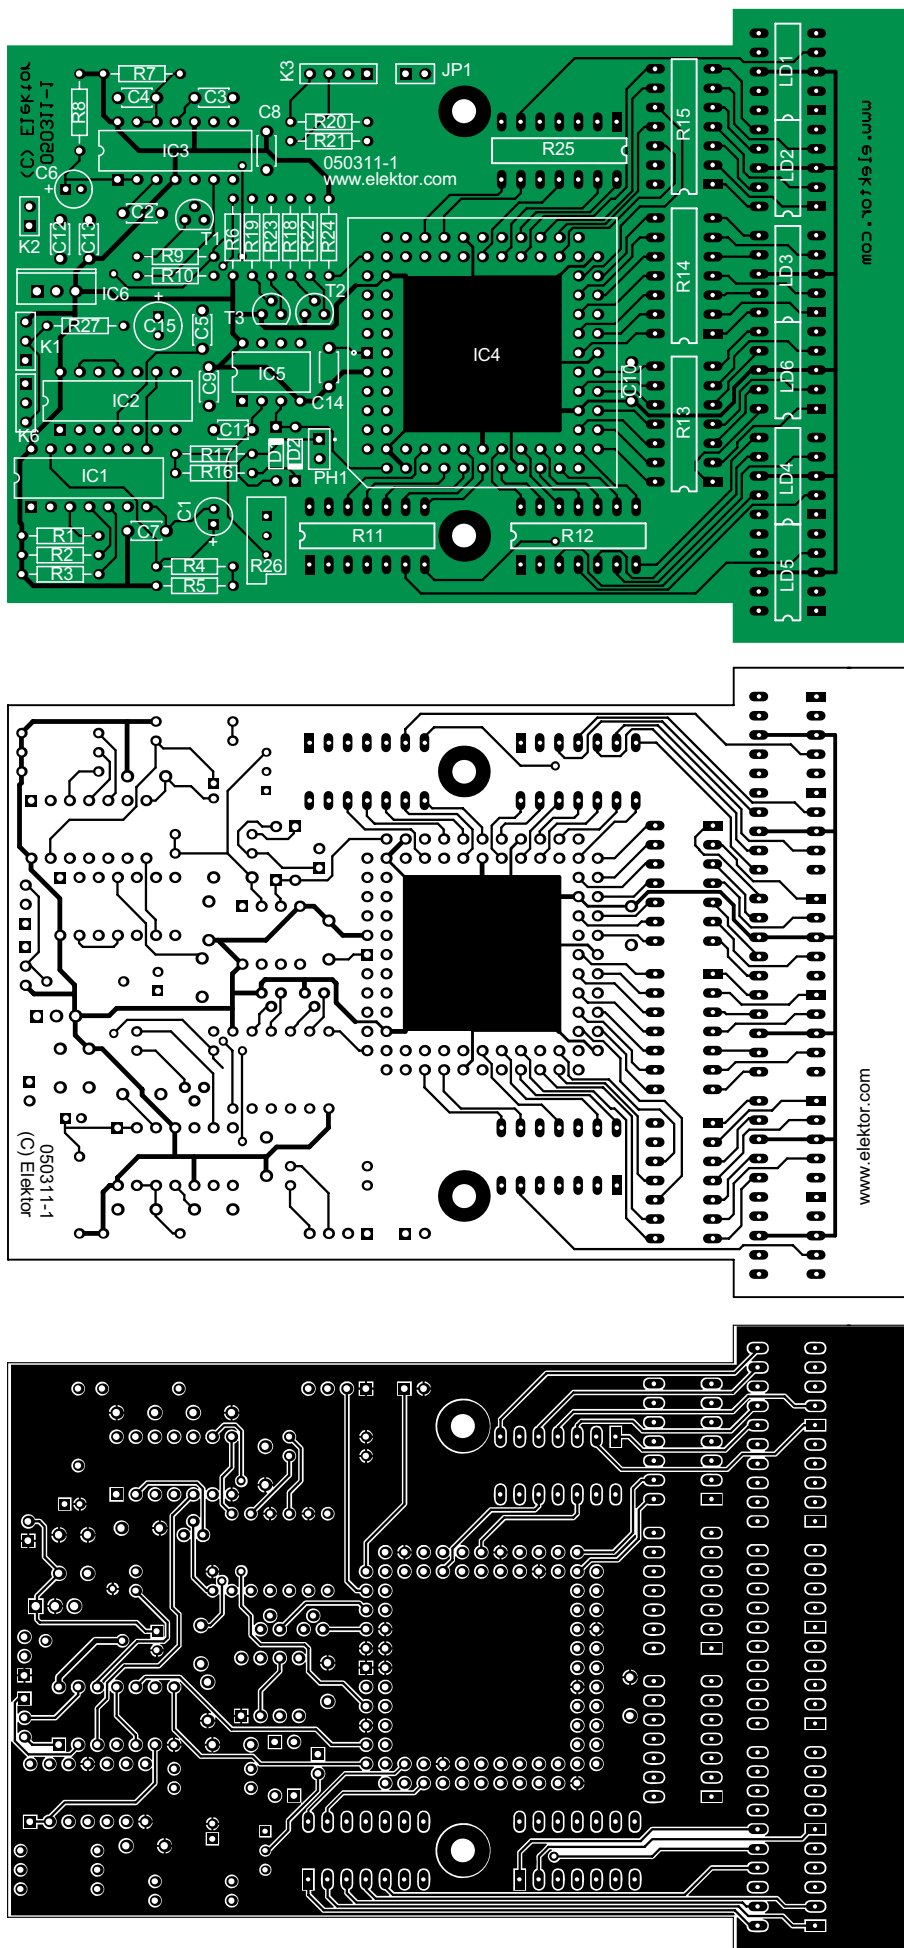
La PCB está diseñada para simplificar la soldadura. El CPLD es el único componente de montaje superficial que se utiliza.
